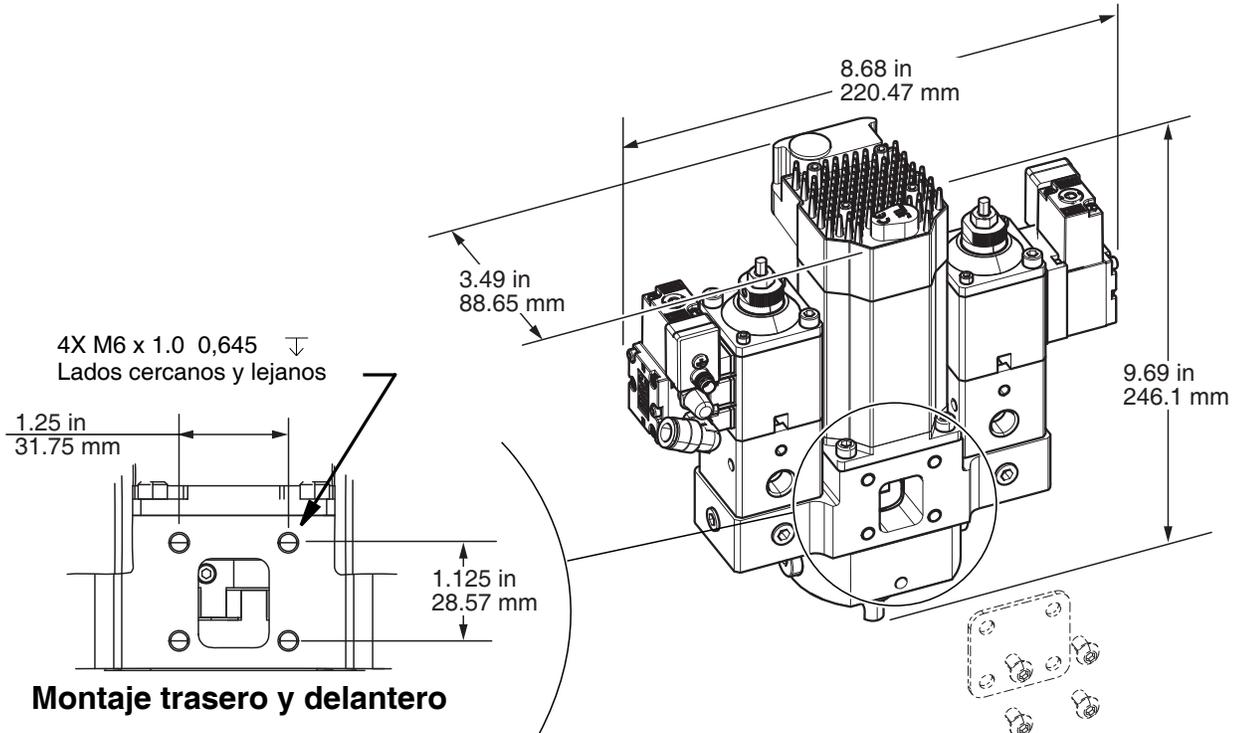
Dimensiones de la válvula de mezcla dinámica Voltex
